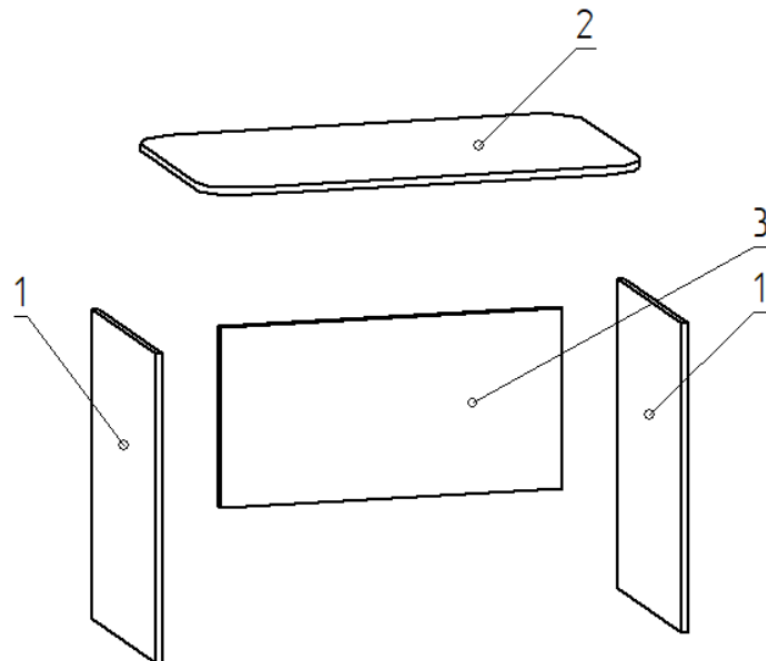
Зразок оформлення креслення столу з розсунутими деталями
